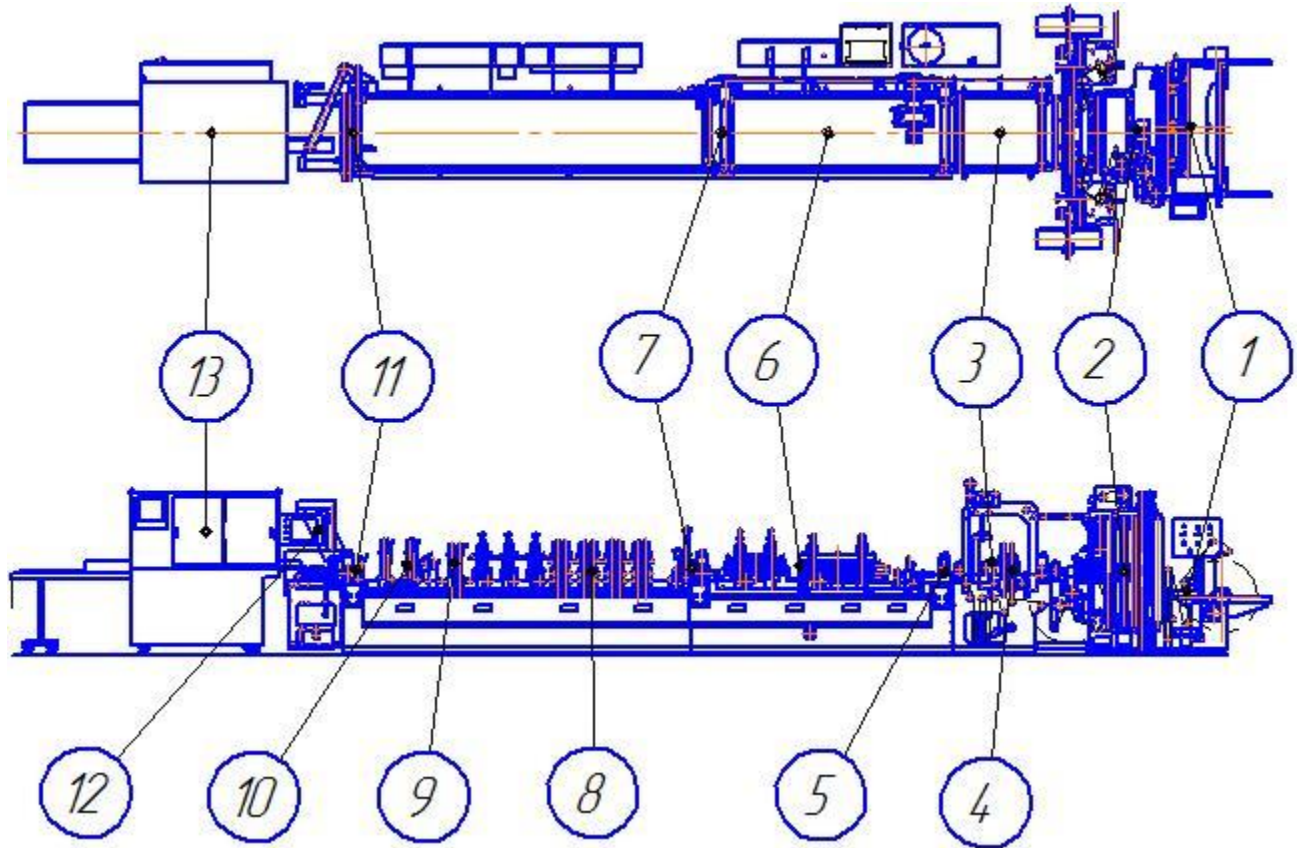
Машина для виготовлення із багатошарових полімерних плівок упаковок типу дой-пак
